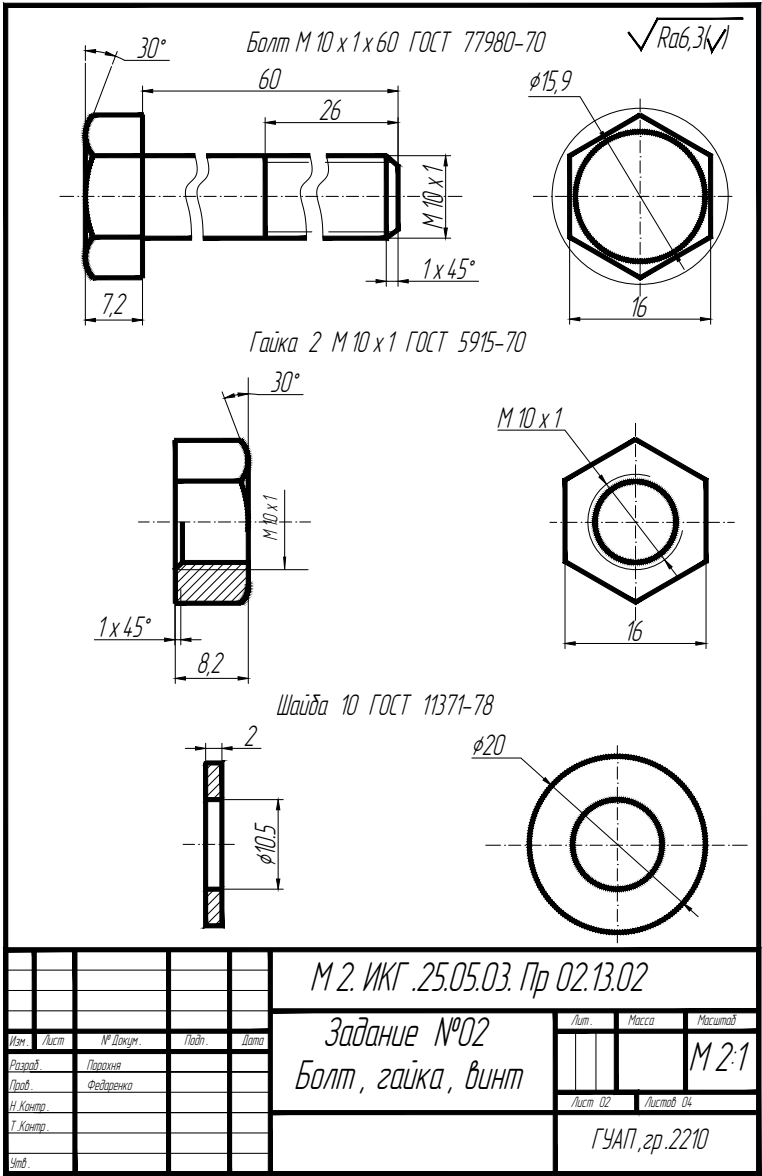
Рабочий чертеж болта, гайки и шайбы
